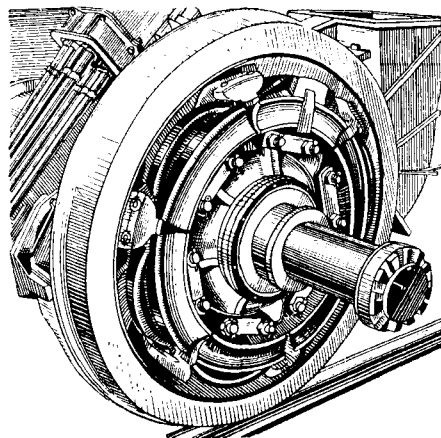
Привод с полым валом и шарнирно-рычажной муфтой с резиновыми втулками (Альстом с шарнирными Silentblock)
